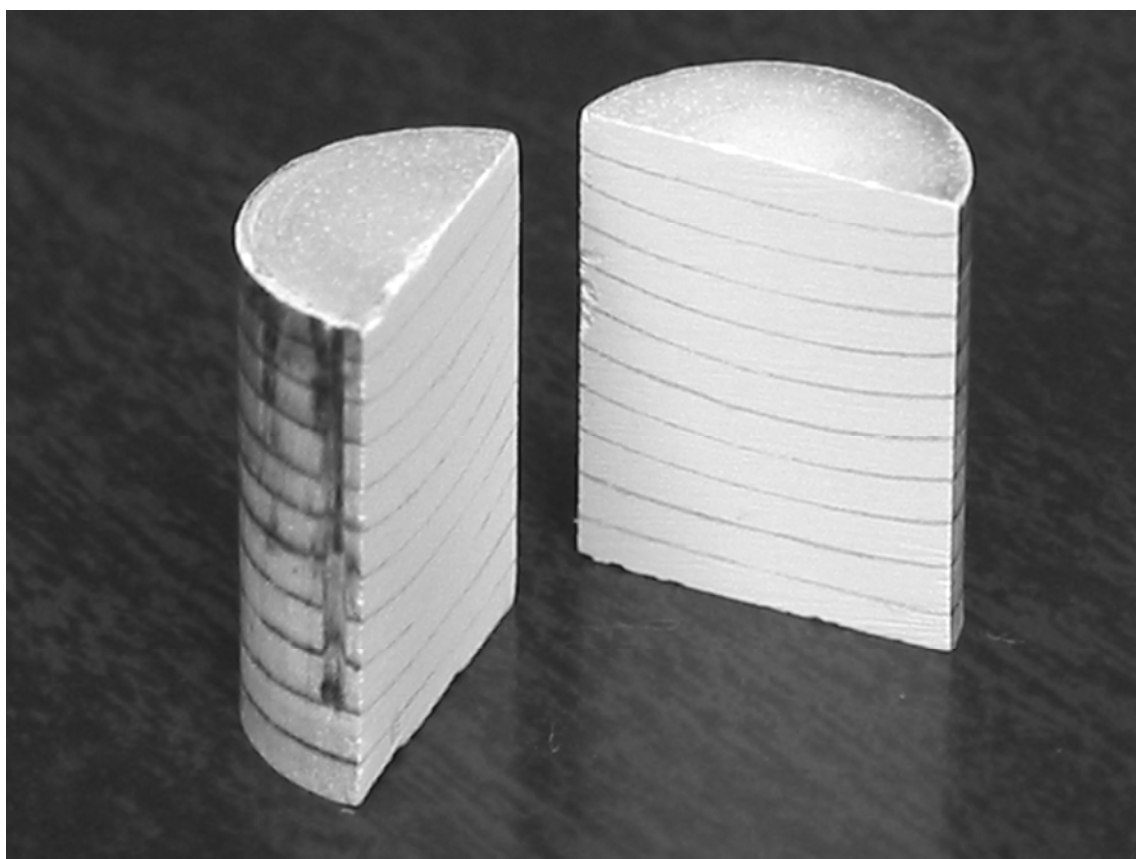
Продольный разрез длинномерной прессовки с маркированными слоями
